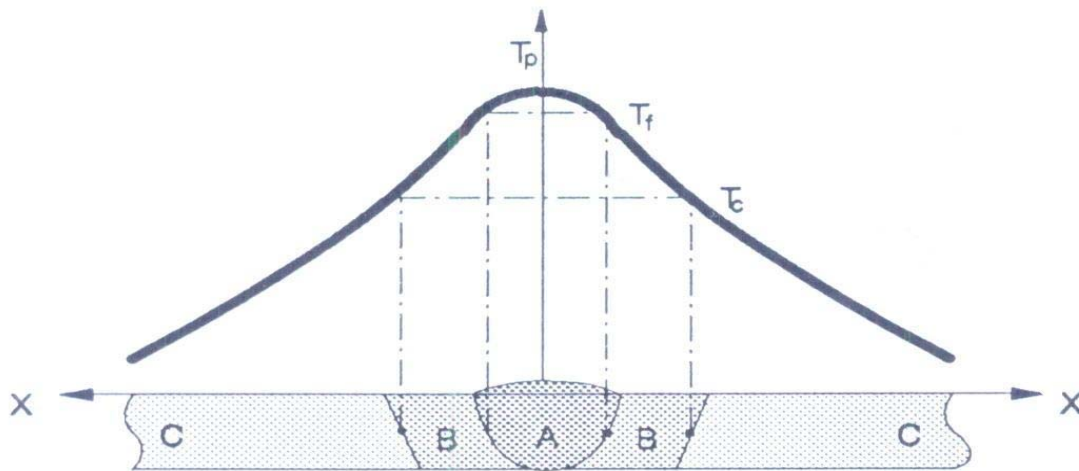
Perfil térmico em um material soldado (Marques, 1991).
